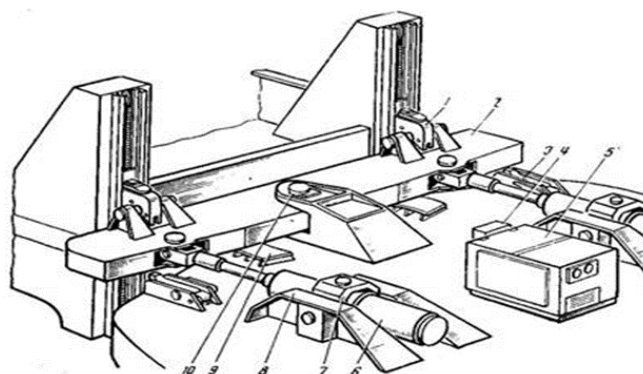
Изгибающее устройство с поворотной балкой.
